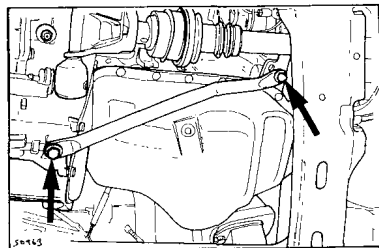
Болты крепления реактивной тяги двигателя (отмечены стрелками)
